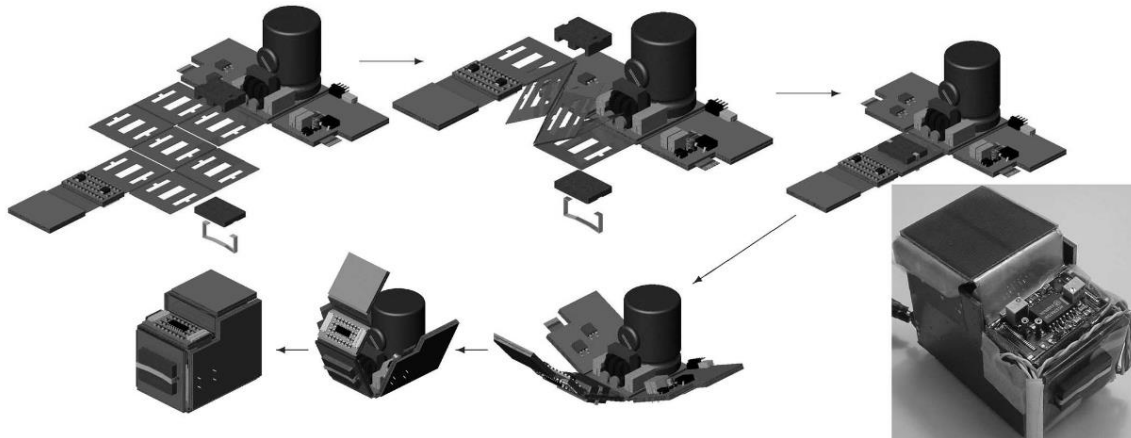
technique de packaging en "3D PCB" proposé par [45].
